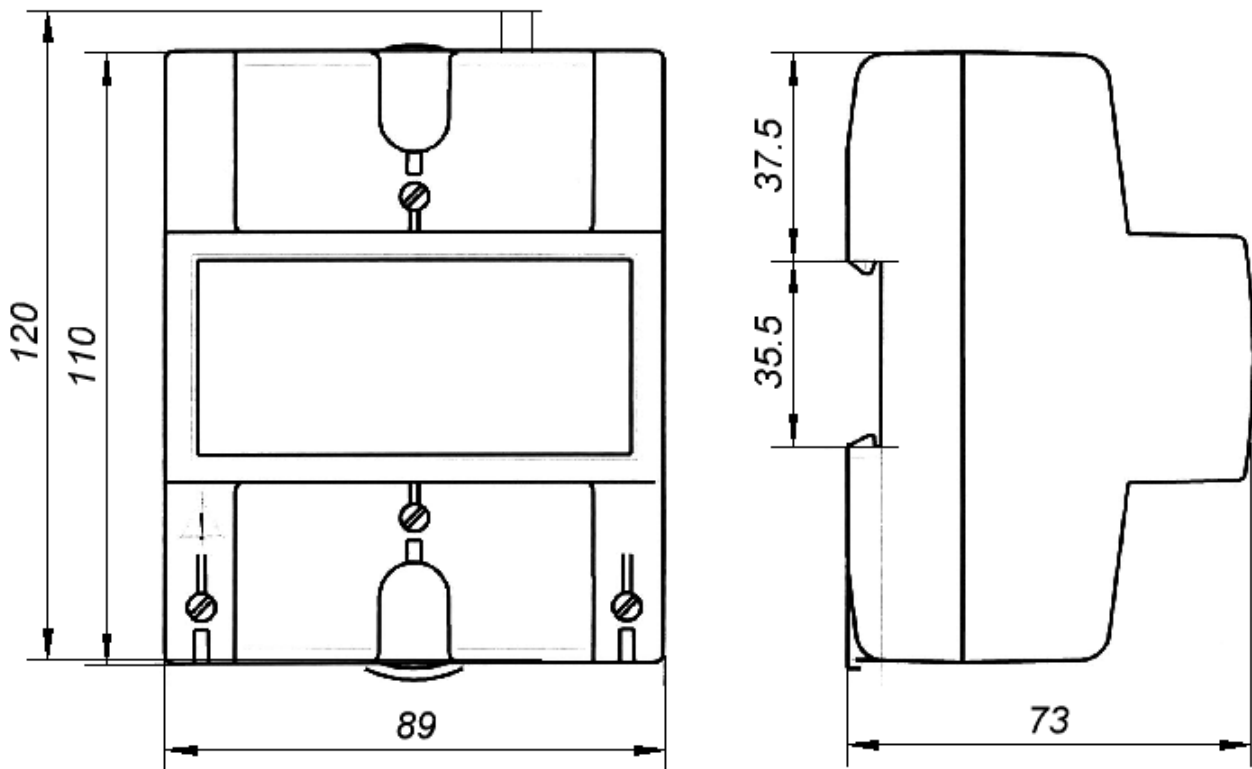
Габаритные и установочные размеры УСПД164-01Б-0, -1
